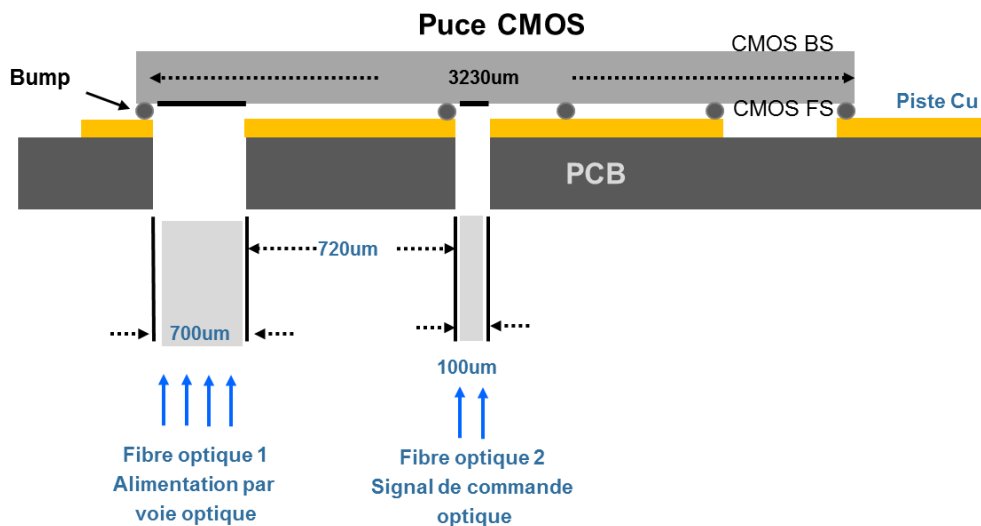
Assemblage flip chip entre la puce CMOS et le PCB.
